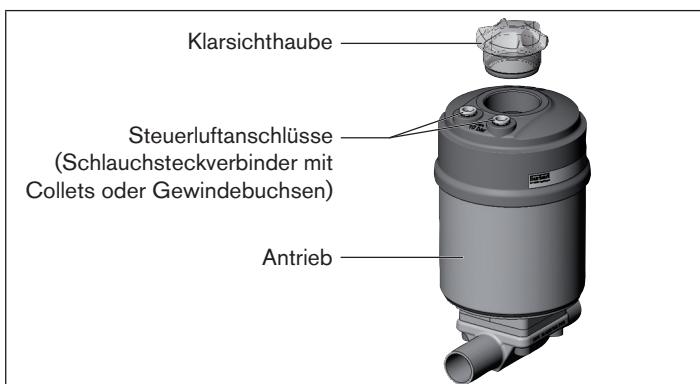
Montage linearer Remote Sensor, Reihe 2103, 2300 und 2301
